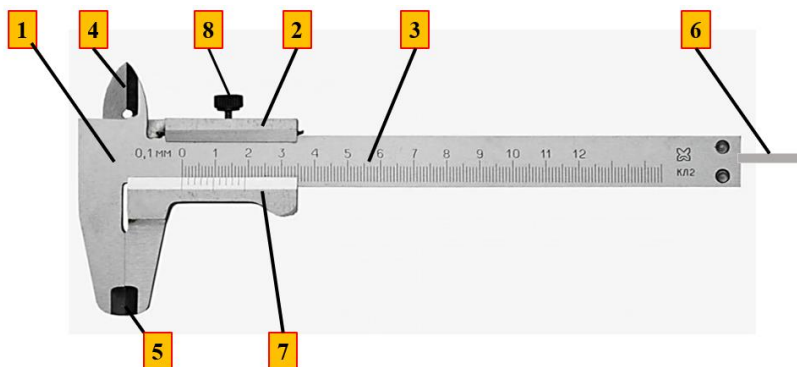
Штангенциркуль: 1 – штанга; 2 – подвижная рамка; 3 – шкала штанги; 4 – губки для внутренних измерений; 5 – губки для наружных измерений; 6 – линейка глубиномера; 7 – нониус; 8 – винт для зажима рамки
